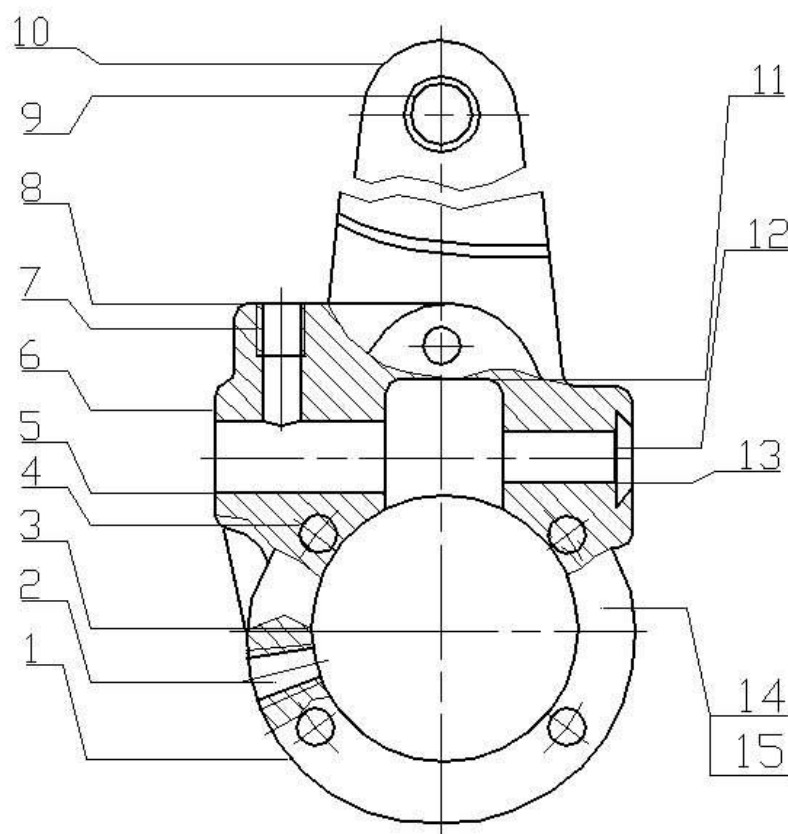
Общий вид детали «Корпус рычага регулировочного»
